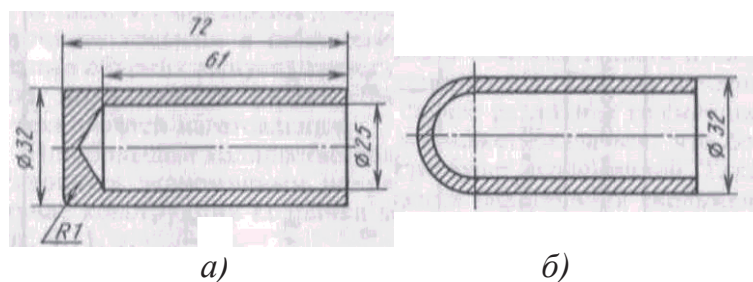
Схема конструкции и обработки колпачка при различных объемах его выпуска: *а* – конструкция колпачка для мелкосерийного производства; *б* – конструкция колпачка для крупносерийного и массового производства
